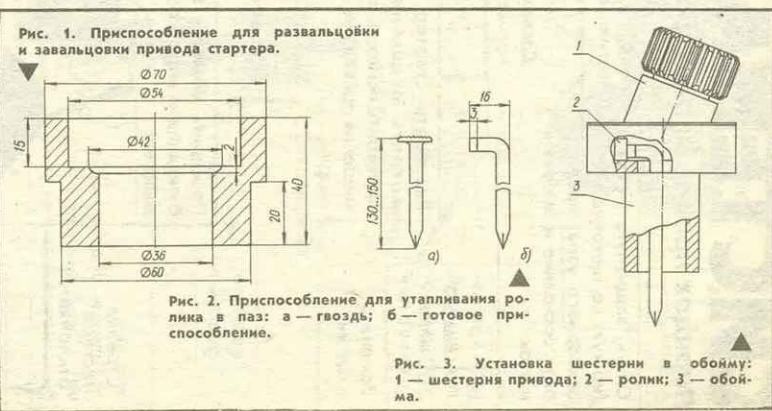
Приспособление для развальцовки и завальцовки привода стартера.
